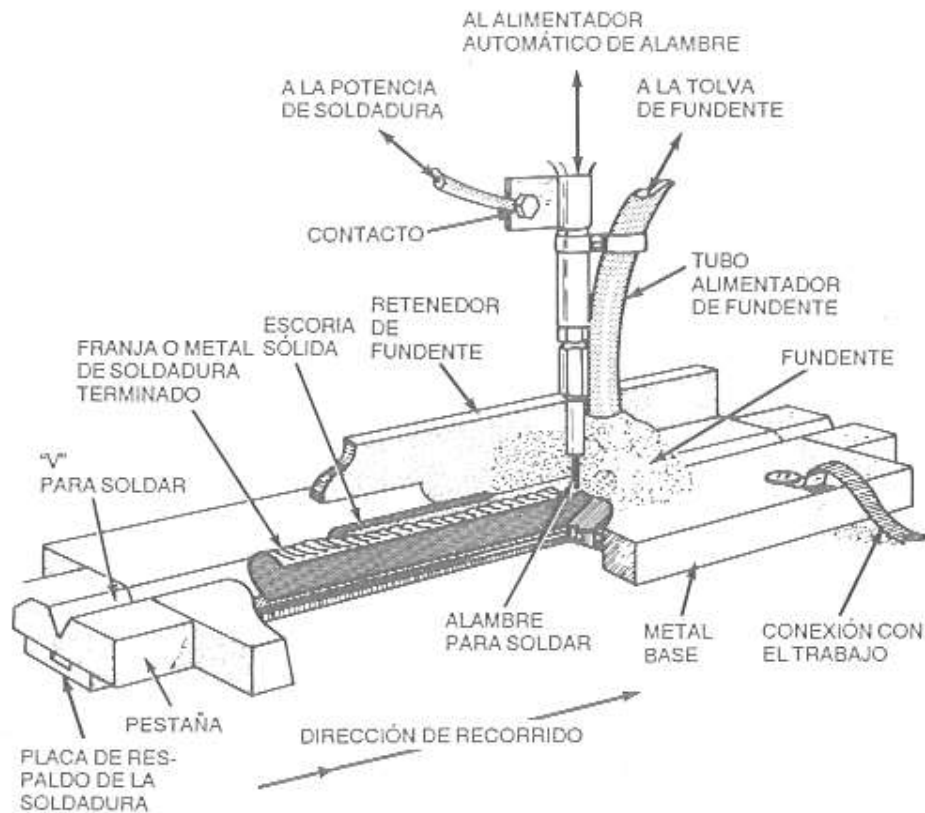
Esquema del proceso de soldadura por arco sumergido SAW.
